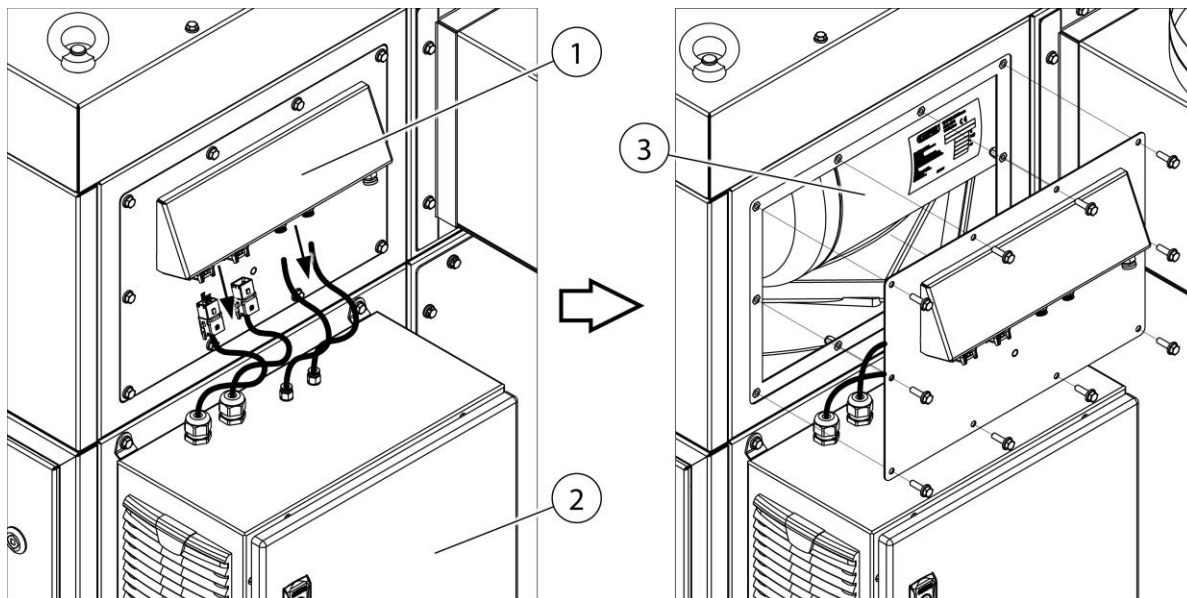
Доступ к резервуару для сжатого воздуха и предохранительному клапану сжатого воздуха
